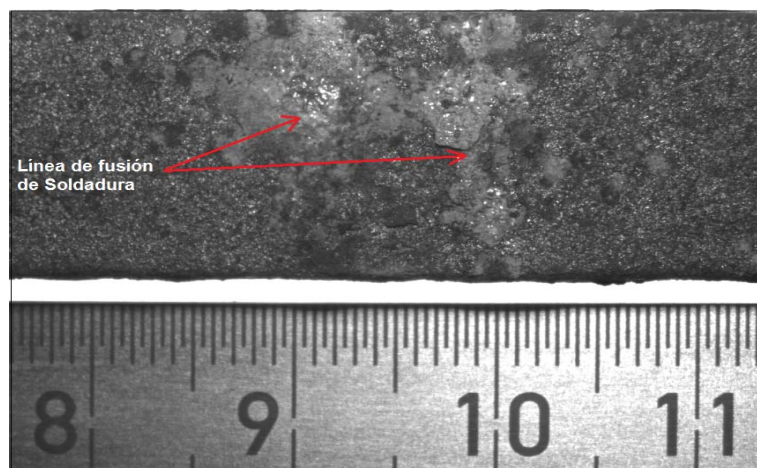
Superficie de la probeta con soldadura SMAW a tensión.
